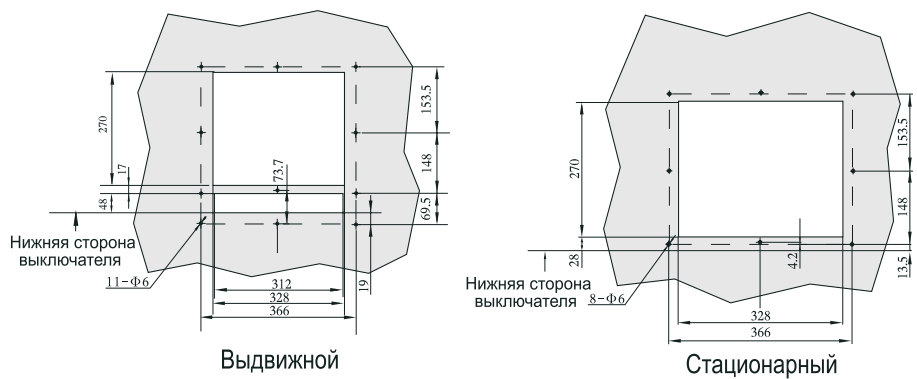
Габаритные размеры рамки обрамления выреза в двери для выключателей типоразмера E
